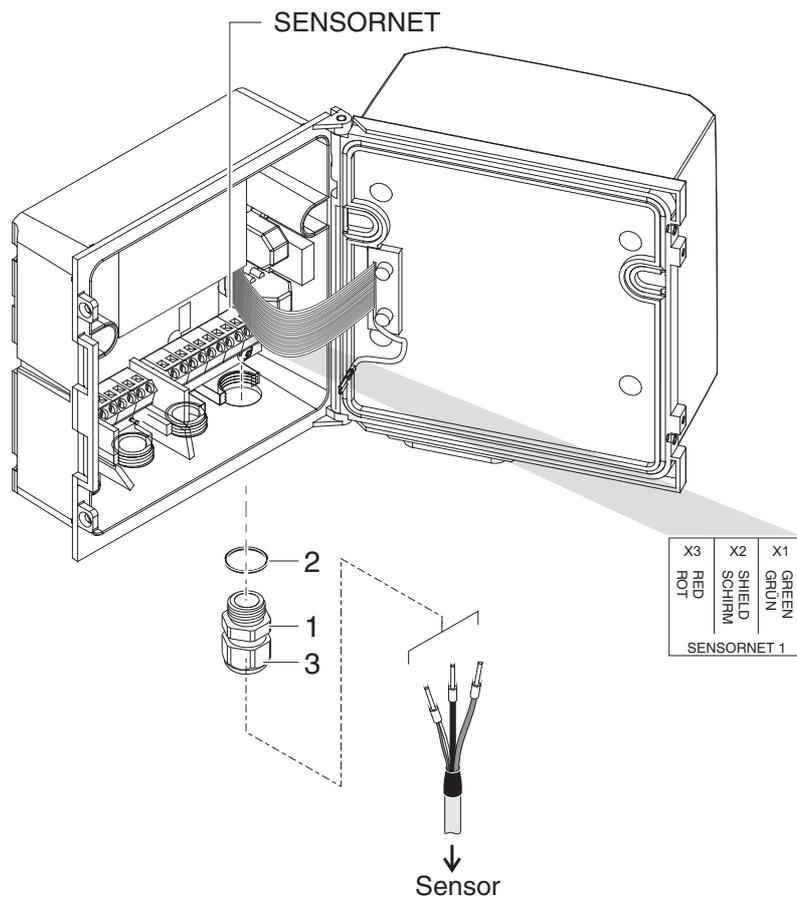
Kabel anschließen (Beispiel DIQ/S 281-CR2)
